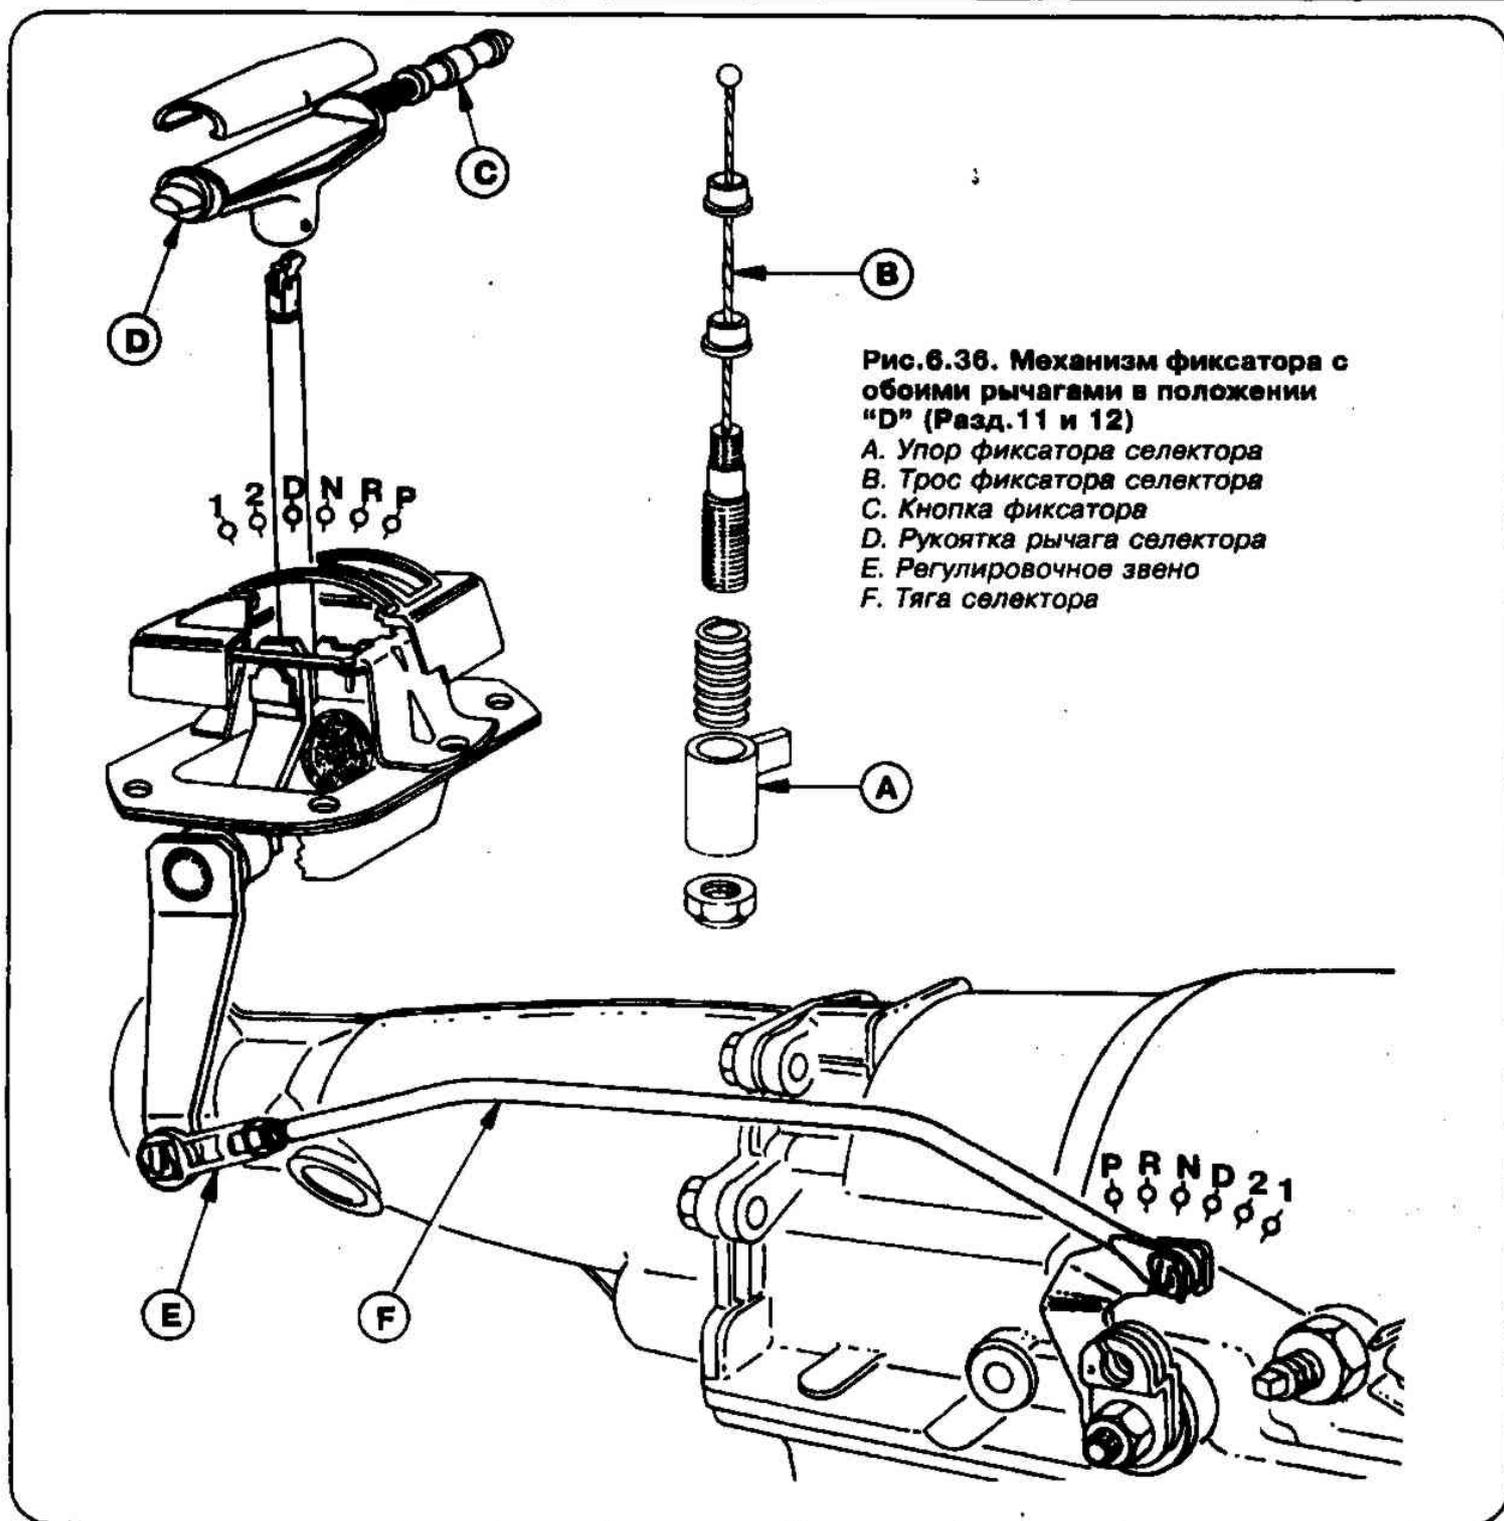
Механизм фиксатора с обоими рычагами в положении "D" (Разд.11 и 12)
